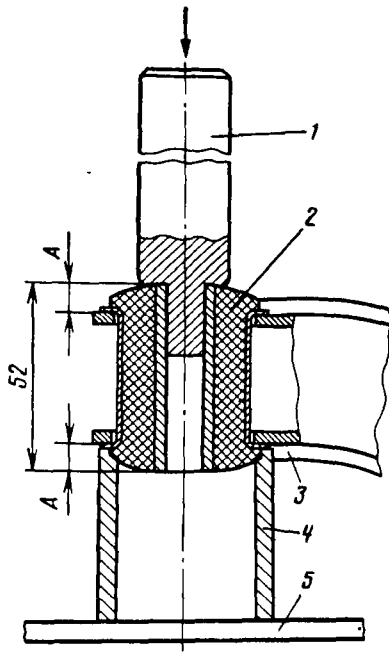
Выпрессовка сайлент-блока из рычага передней подвески:
